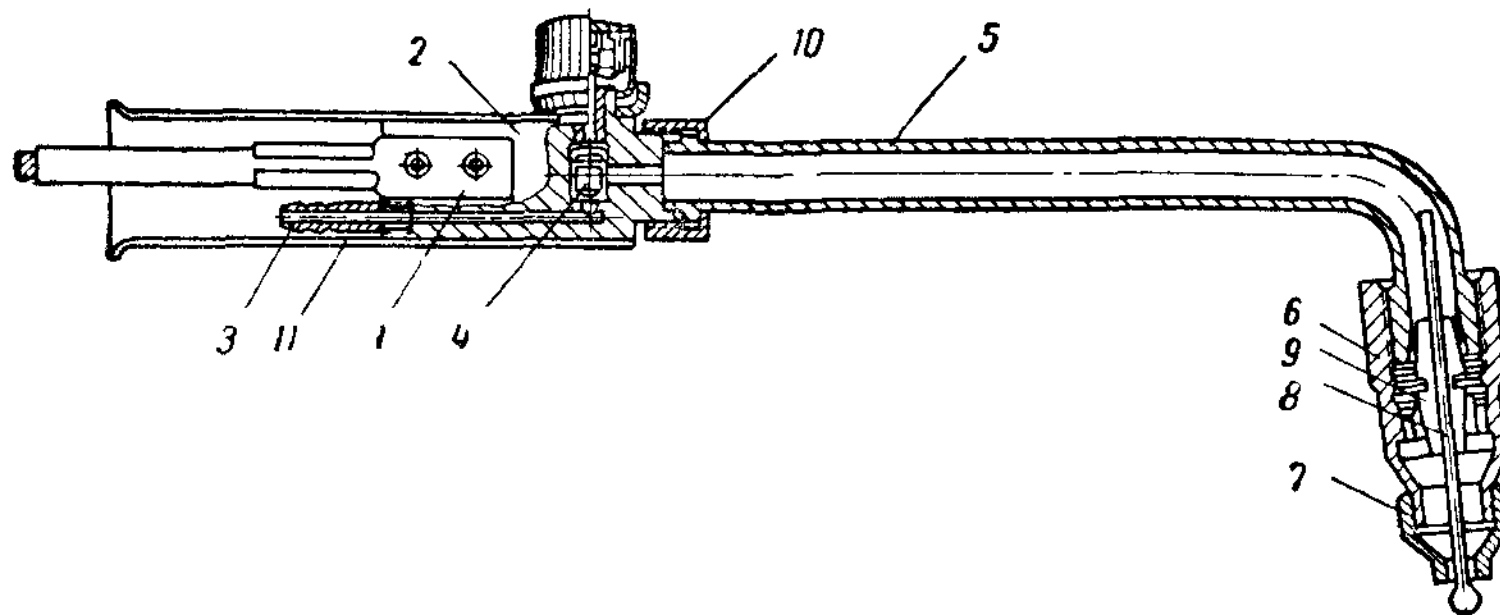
Ручная горелка для аргоно-дуговой сварки
